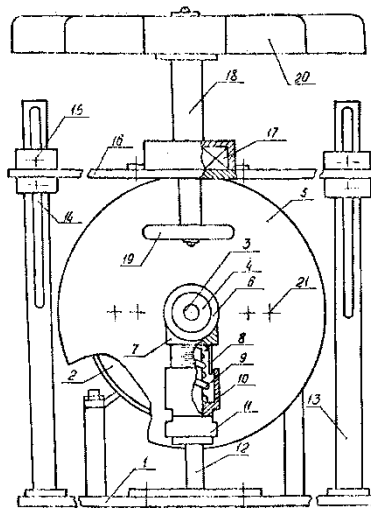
Нагрузочное устройство для форсирования статических и динамических нагрузок на подшипники и обмотки статора
